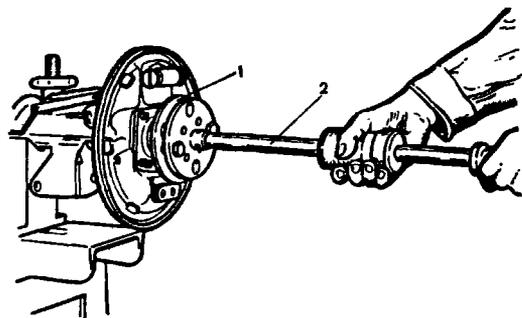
Выпрессовка полуоси с помощью съемника 67.7801.9516: 1 - полуось; 2 - ударный съемник
